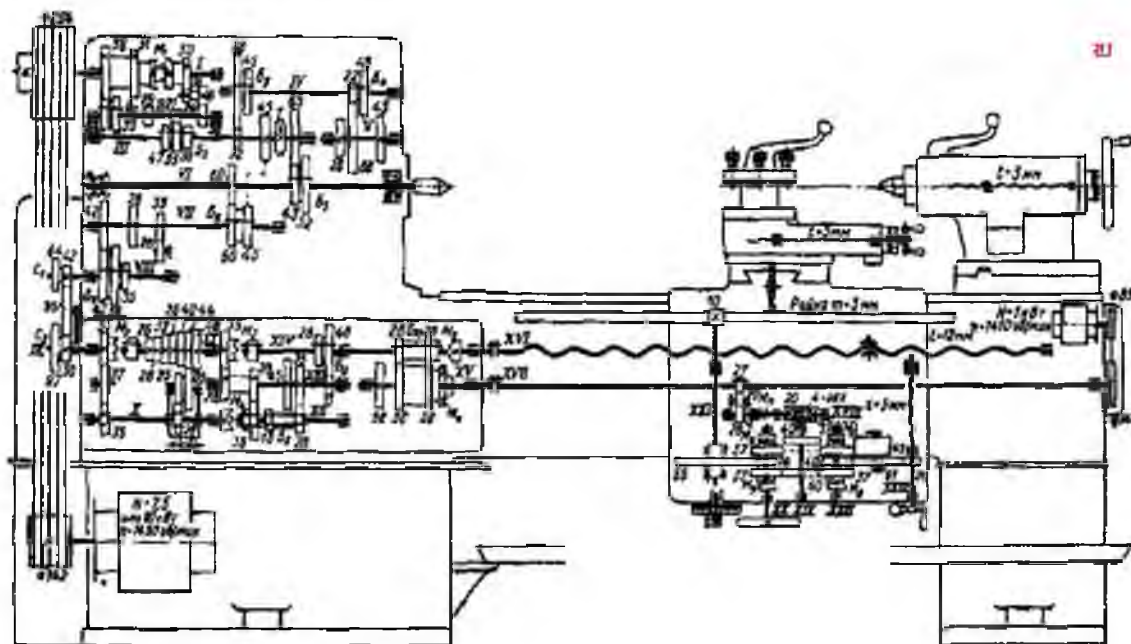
Кинематическая схема токарно-винторезного станка модели 1K62.
